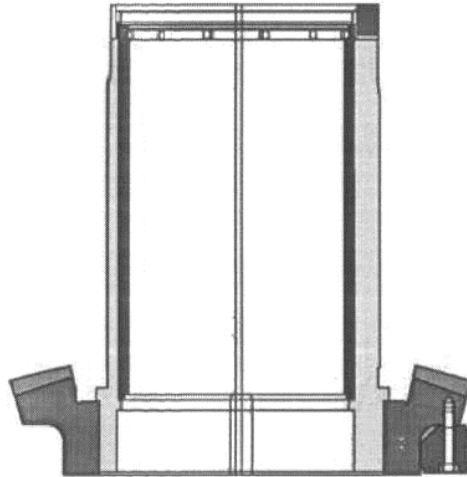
Верхня противага дробарки Metso Superior MK-II 54-75
